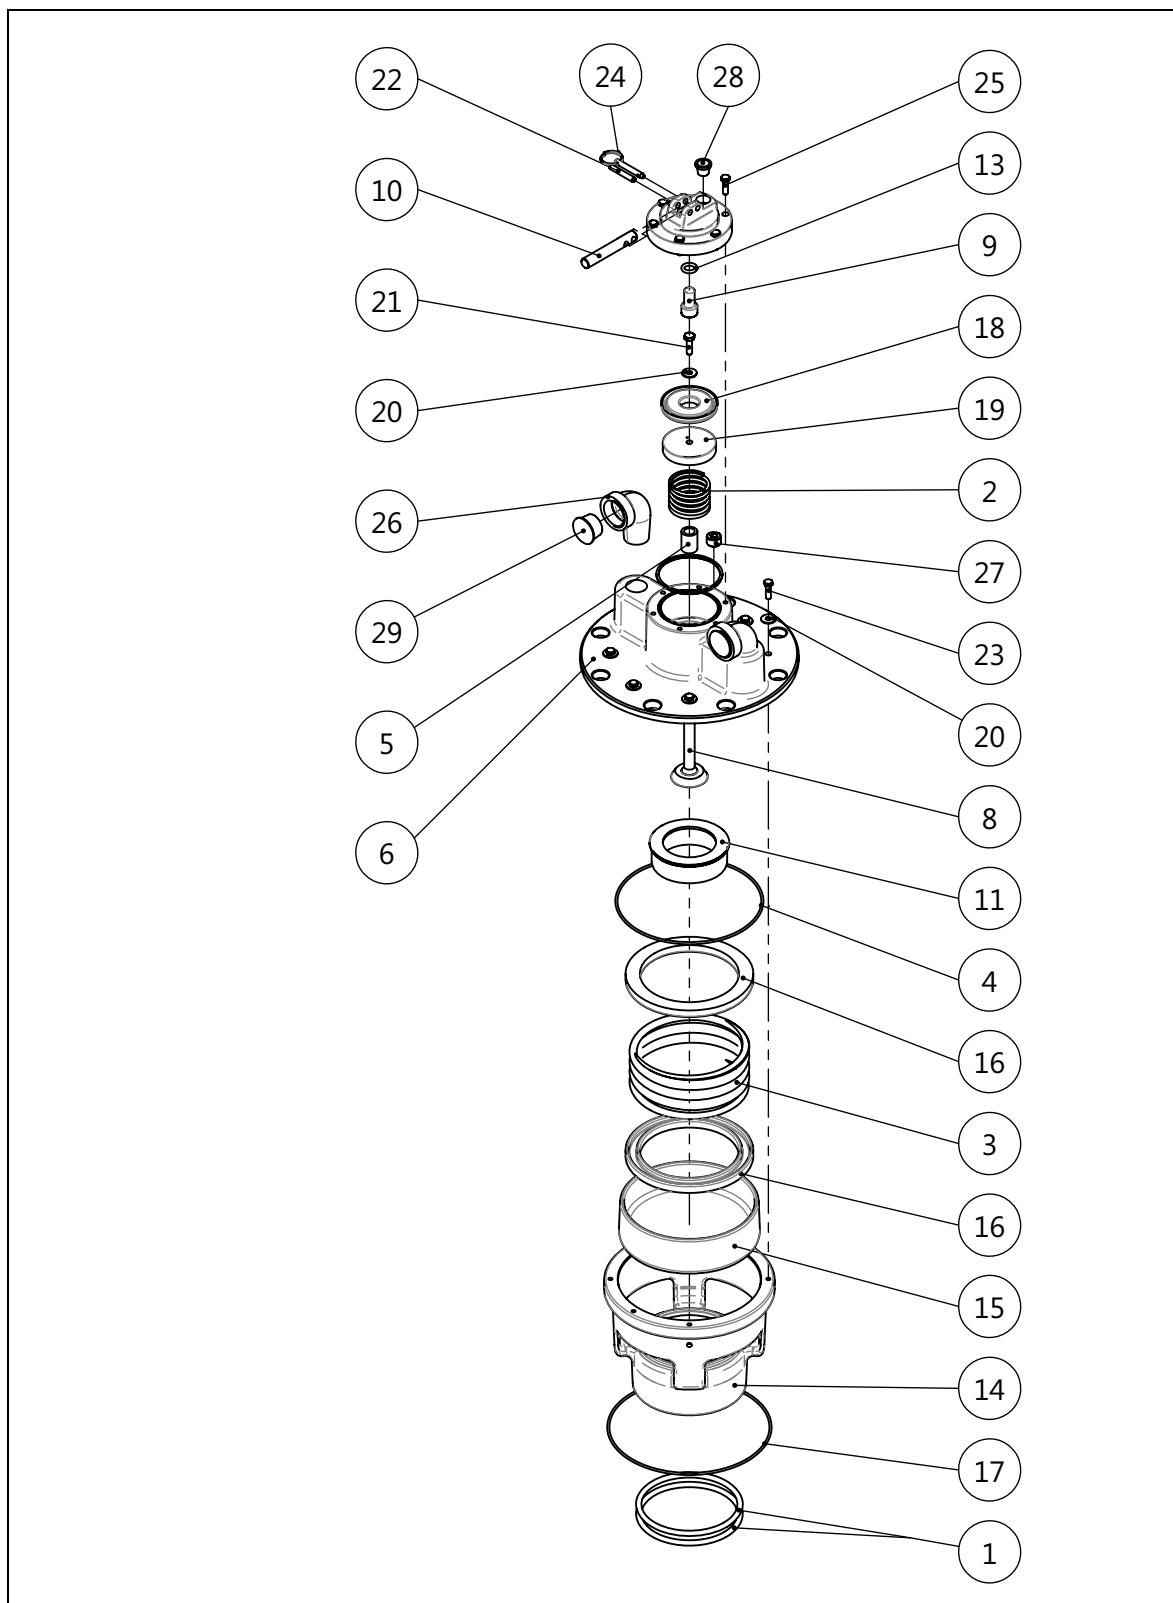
Номера деталей крышки вентиляционного клапана MARTIN® Hurricane
